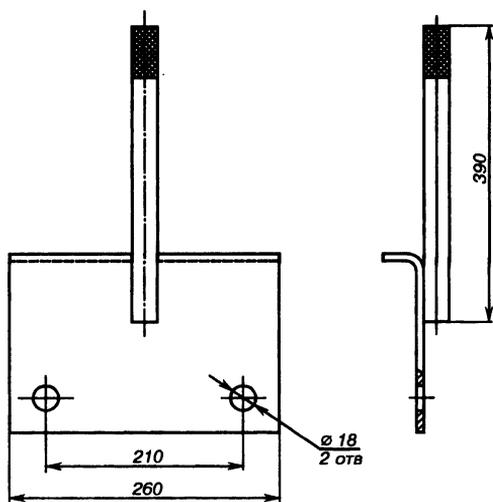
Кронштейн двойного крепление фазы на угловой опоре ВЛ 6–10 кВ
